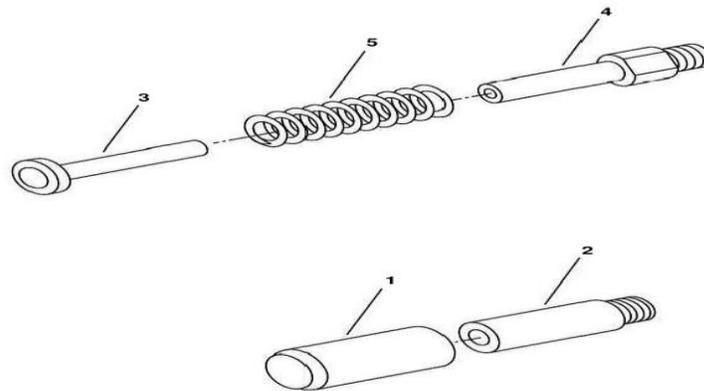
Componentes del pistón de control de las bombas de pistones Rexroth A10vO series 31. [18]
